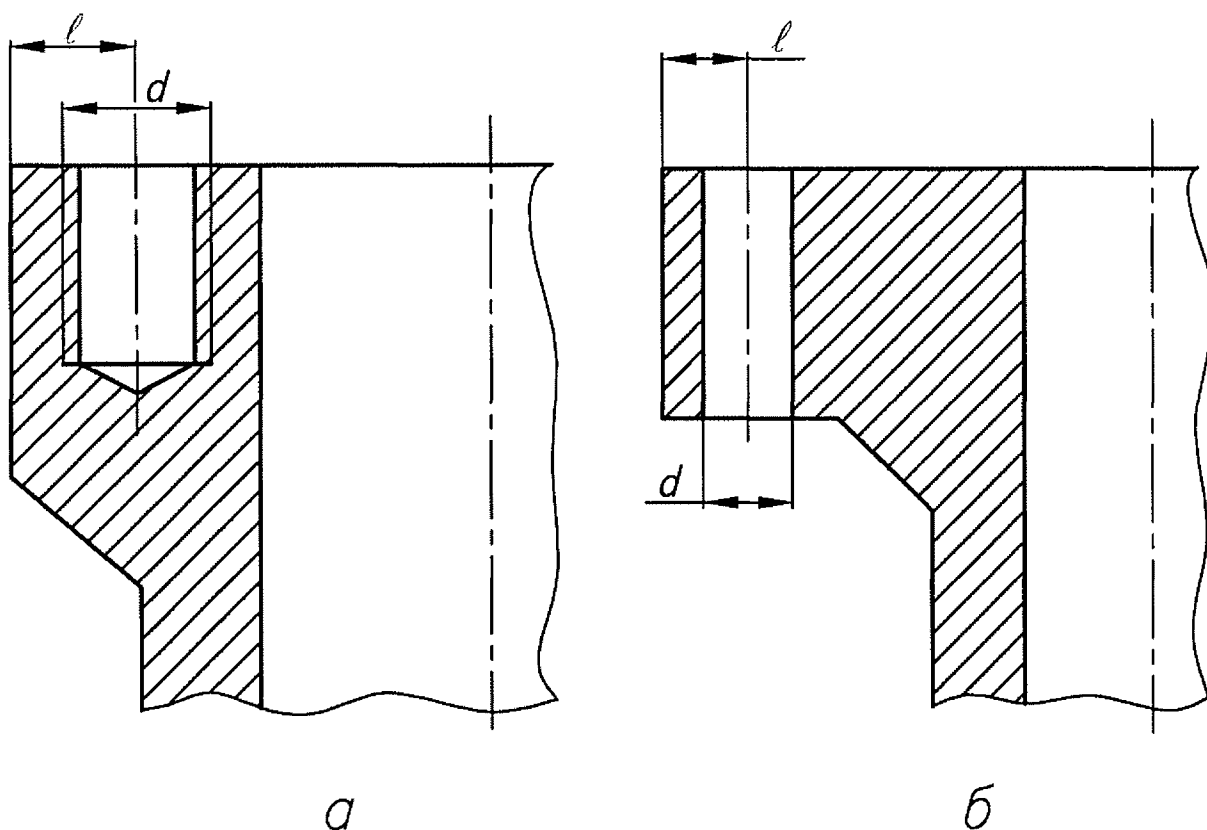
Расположение отверстий под шпильки (а) и болты (б)
